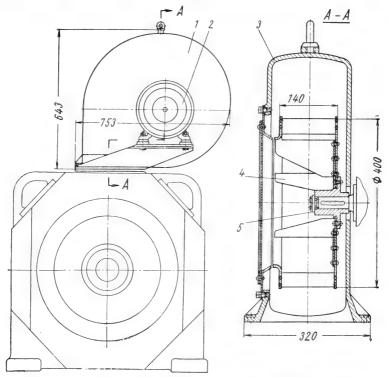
Установка вентилятора на двигателе подъемной лебедки
